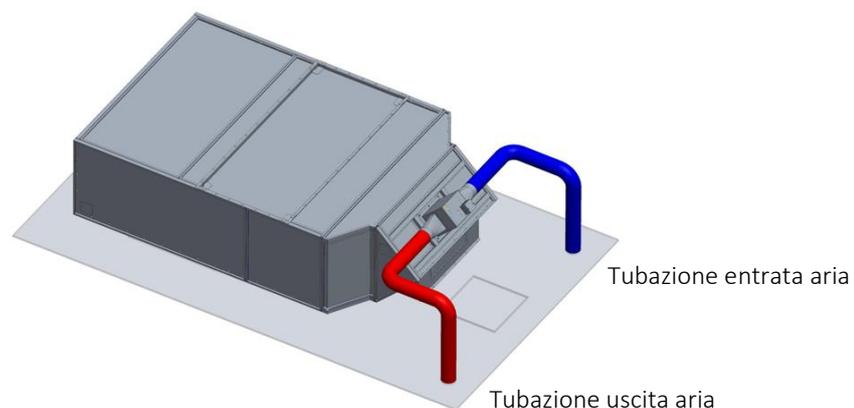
Schema di collegamento del sistema di ventilazione: vista dall'alto.
